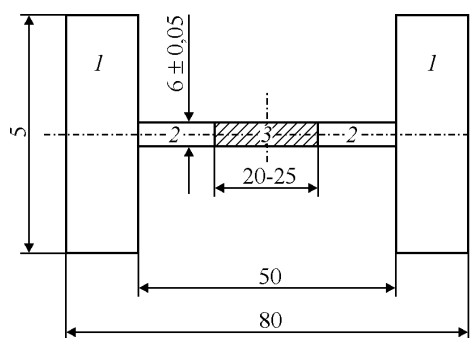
Размеры (в мм) и составные части металлической заготовки.
